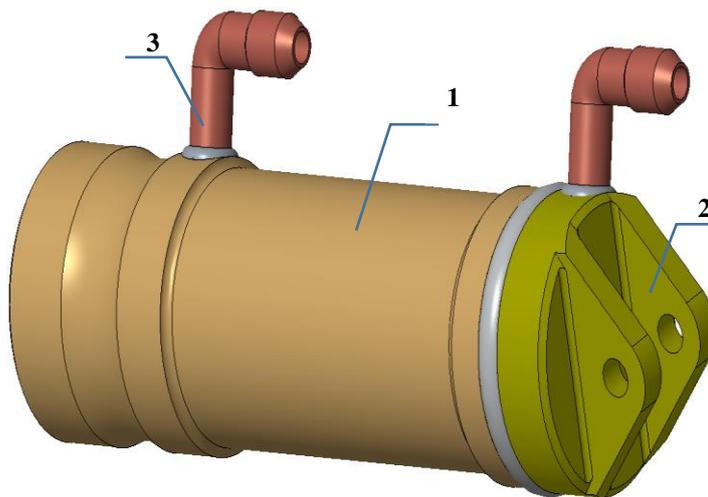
3D-модель цилиндра гидроусилителя руля:
